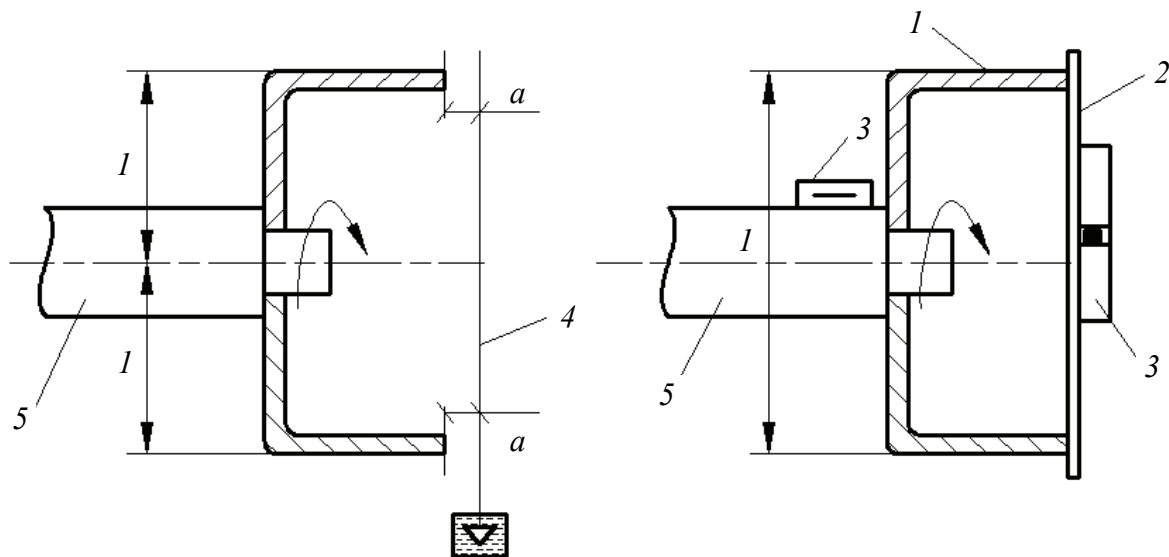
Схемы проверки горизонтальности вала: 1 – скоба; 2 – пластина; 3 – уровень; 4 – отвес; 5 – вал
